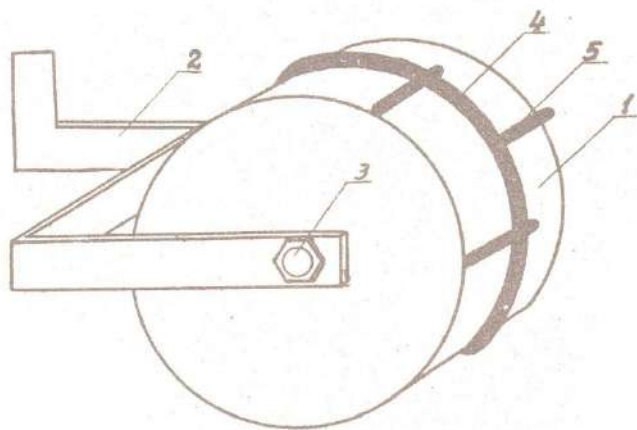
Каток-бороздодел с продольными и поперечными выступами: 1- корпус, 2-вилка, 3-ось, 4-продольный выступ, 5-поперечный выступ.
